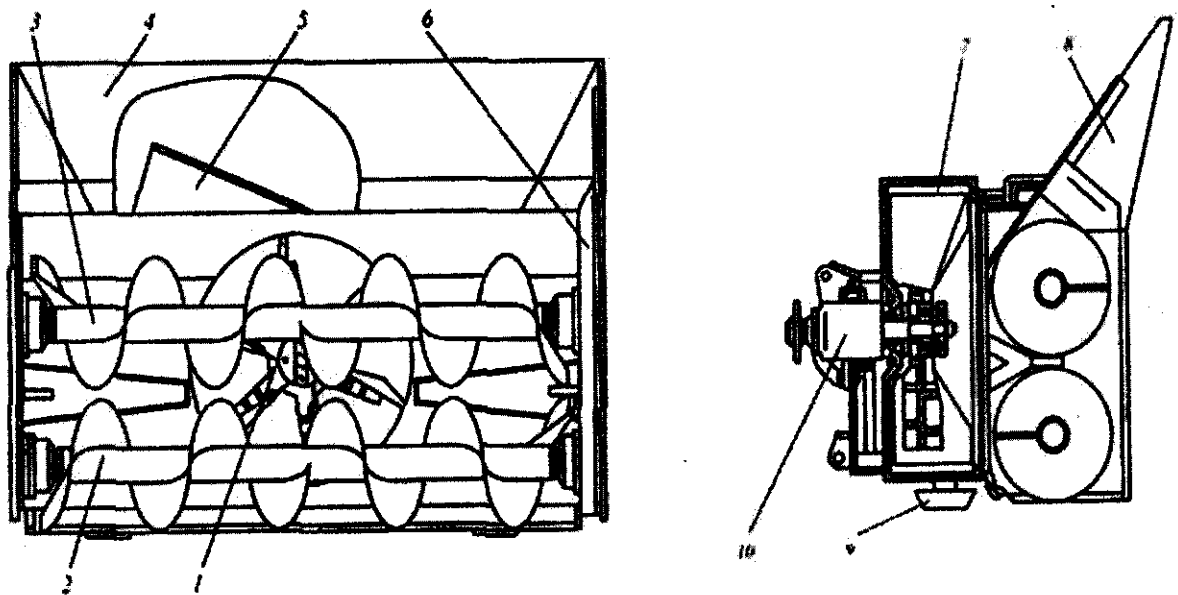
Шнекороторное оборудование снегопогрузчика (1 - нижний шнек, 2 - ротор снегометателя. 3 - верхний ротор, 4 - кожух шнековой камеры, 5 - направляющий аппарат снегометателя, 6 - кожух редуктора привода шнеков; 7 - кожух снегометателя; 8 - козырек, отбрасывающий снег в зону работы шнеков; 9 - опорная лыжа; 10 - редуктор привода ротора)
